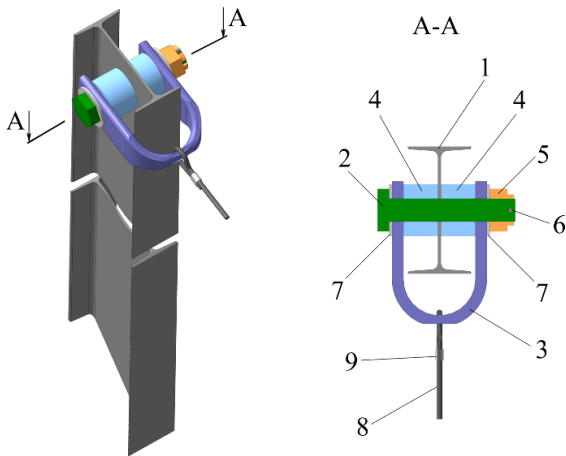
Конструкция стальной балки для крепления анкерного каната:
